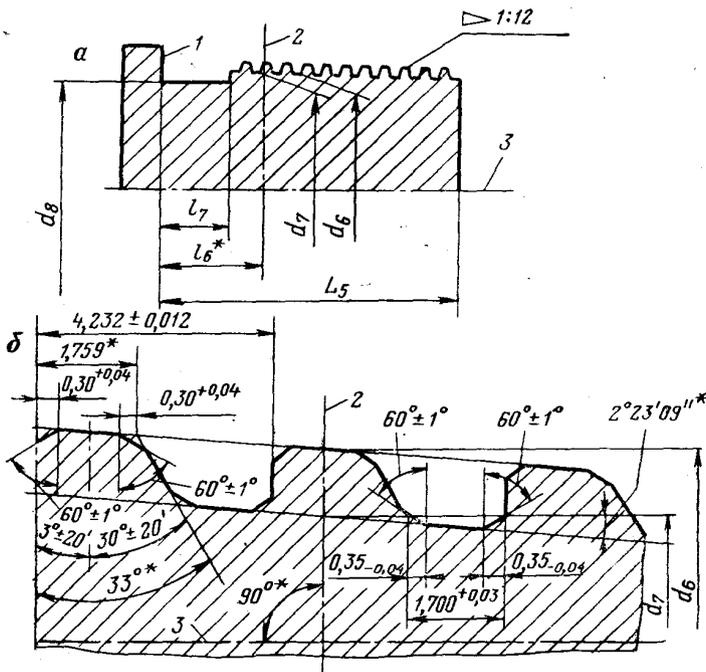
Калибр-пробка Р для контроля профиля и внутреннего диаметра резьбы:
